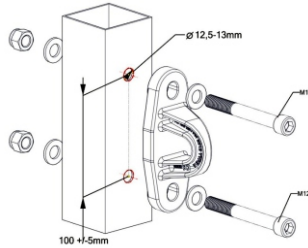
Установка болтовых креплений с анкерной точкой на стальную конструкцию.
